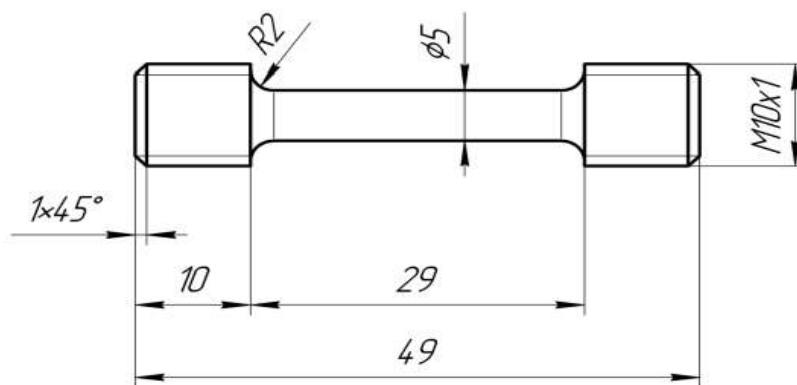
Геометрія гладкого циліндричного зразка.
